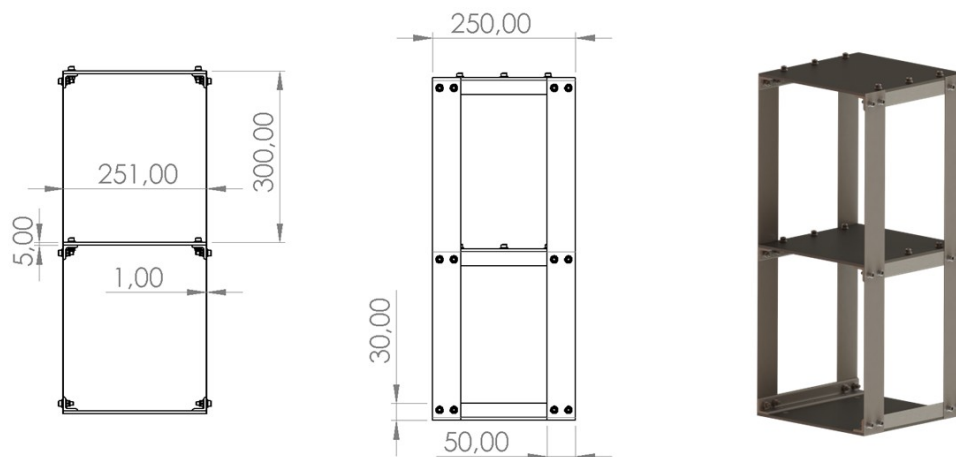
Desenho técnico e vista isométrica do pórtico estrutural / Figure 2 – Technical drawing and isometric view of the structural frame.
